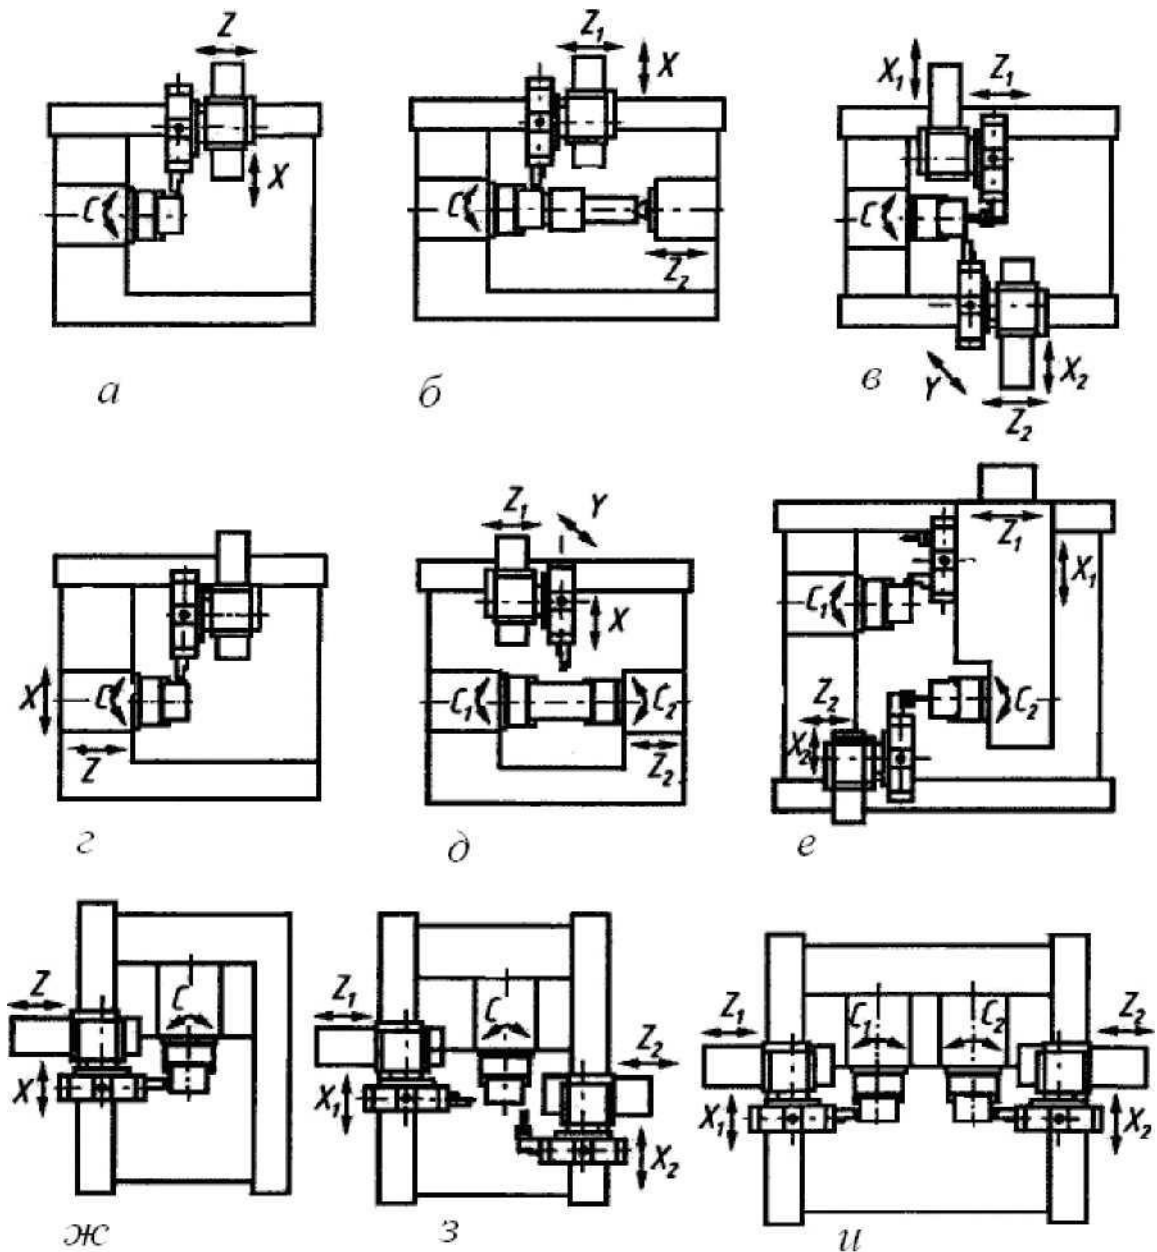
Компонувальні схеми верстатів токарної групи з горизонтальною віссю обертання оброблюваної деталі (*a....e*) і з вертикальною віссю обертання оброблюваної деталі (*ж....и*)
